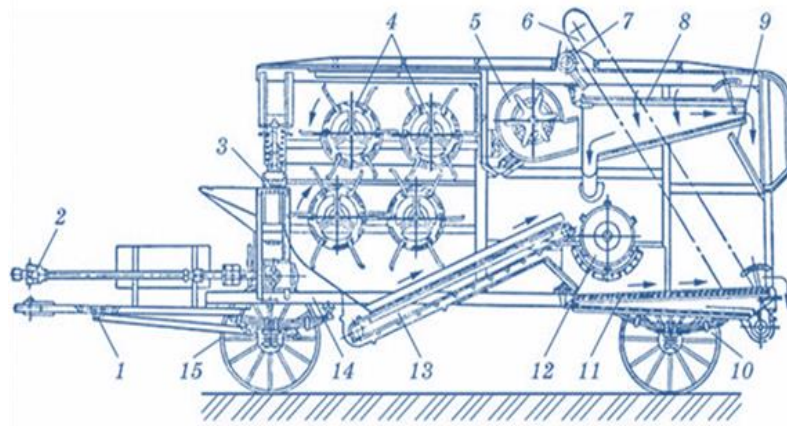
Коноплемолотарка МЛК-4,5А: 1 – причіпний пристрій; 2 – карданна передача; 3 – затискний конвеєр; 4 – обчисувальний апарат; 5 – вентилятор; 6 – елеватор; 7 – шнек; 8 – решітний стан; 9 – скатна дошка; 10 і 15 – опорні колеса; 11 – грохот; 12 – терковий апарат; 13 – конвеєр вороху; 14 – рама.
